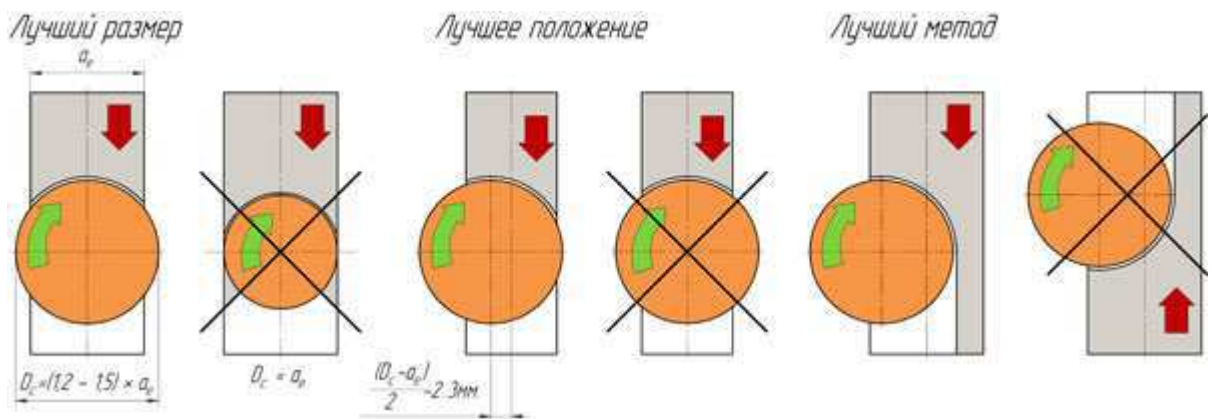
Варианты расположения фрезы относительно заготовки
